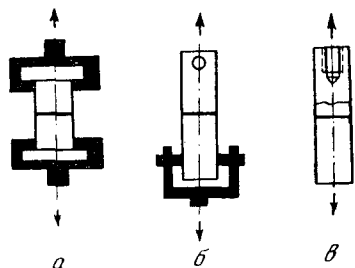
Образцы для измерения прочности склеивания металлов: а — цилиндрические образцы — грибки; б — цилиндрические или призматические образцы с осевым креплением; в — то же с резьбовым креплением.
